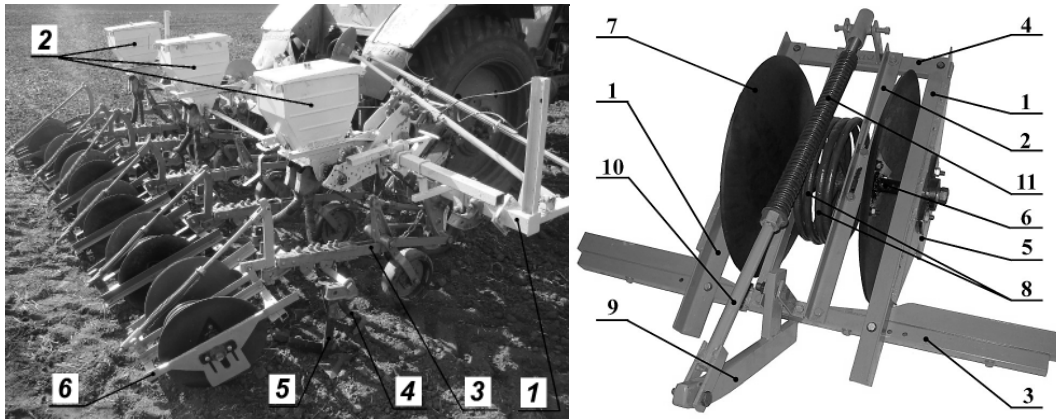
Комбінований посівний агрегат: каток-гребнеутворювач: 1 – бокові балки; 2 – поздовжні балки; 3 – передня балка; 4 – задня балка; 5 – пластина з прорізами; 6 – піввісь; 7 – сферичні диски; 8 – прикочувальні кільця; 9 – кронштейн; 10 – штанга; 11 – пружина
